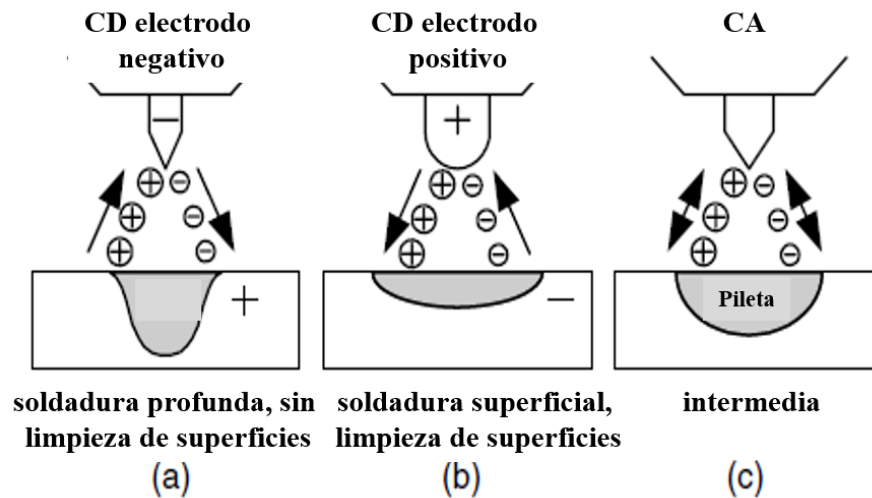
Tipos de polaridad en el proceso de soldadura GTAW [58].
